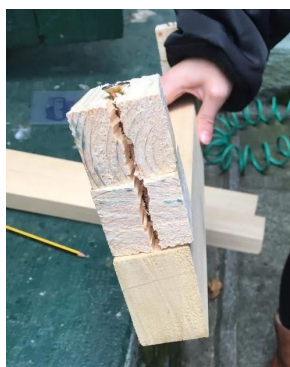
nicht so einfach, Schrauben ins Holz zu bringen
